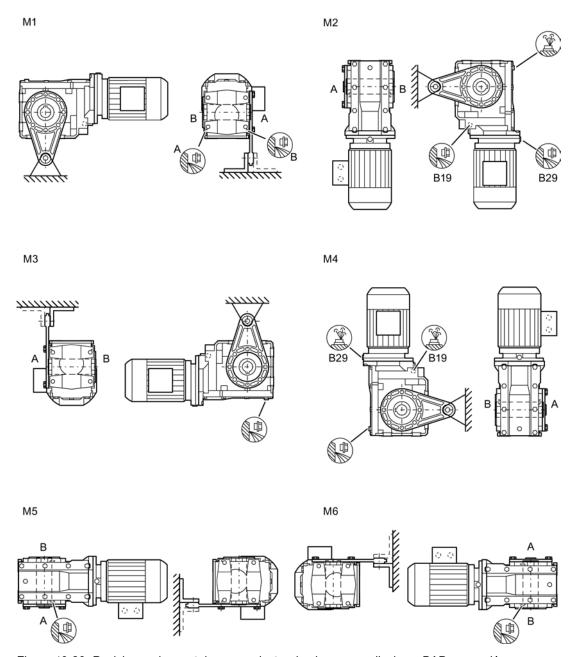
Posiciones de montaje para reductor de ejes perpendiculares BAD en versión enchufable, tamaños 19 - 29
